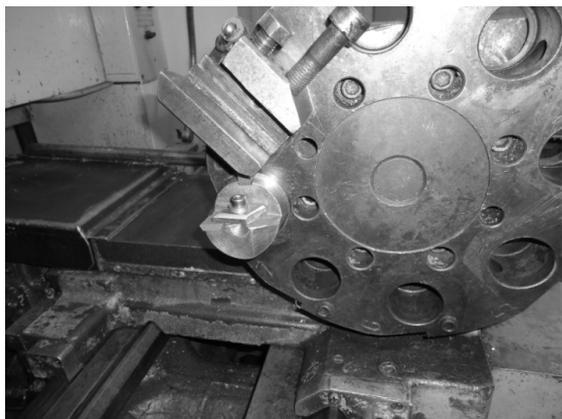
МИО в револьверной головке станка 16К20Ф3
